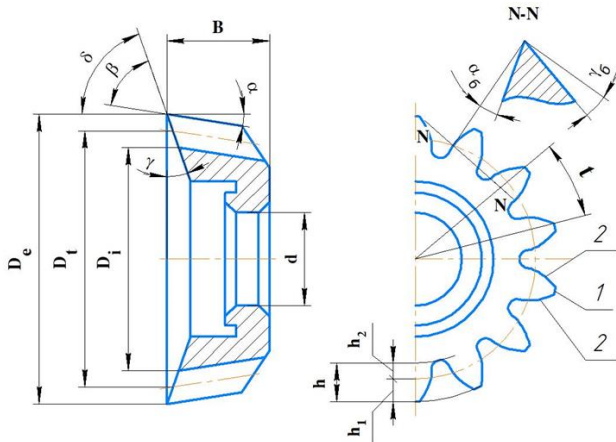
Конструктивные параметры долбяка: D_e - наружный диаметр; D_i - внутренний диаметр; D_t - делительный диаметр; h_1 - высота головки; h_2 - высота ножки; h - высота зуба; t - шаг.
